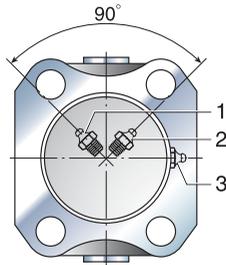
Расположение пресс-масленок карданного вала (вид со стороны моста): 1 — масленка шарнира со стороны раздаточной коробки; 2 — масленка шарнира со стороны моста; 3 — масленка шлицевого соединения
